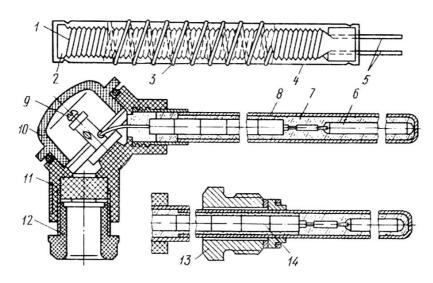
Платиновый термопреобразователь сопротивления: 1 — платиновая проволока; 2 — каркас; 3 — серебряная лента; 4 — слюдяная пластинка; 5 — выводы; 6 — чувствительный элемент; 7 — оксид аммония; 8 — защитная арматура; 9 — зажим; 10 — крышка; 11 — головка; 12, 13 — штуцера под кабель и штуцер для крепления оправы; 14 — изоляторы
